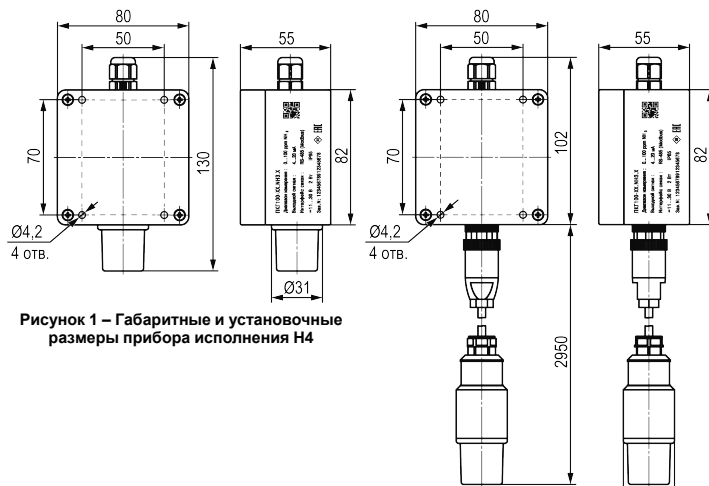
Габаритные и установочные размеры прибора исполнения Н4
